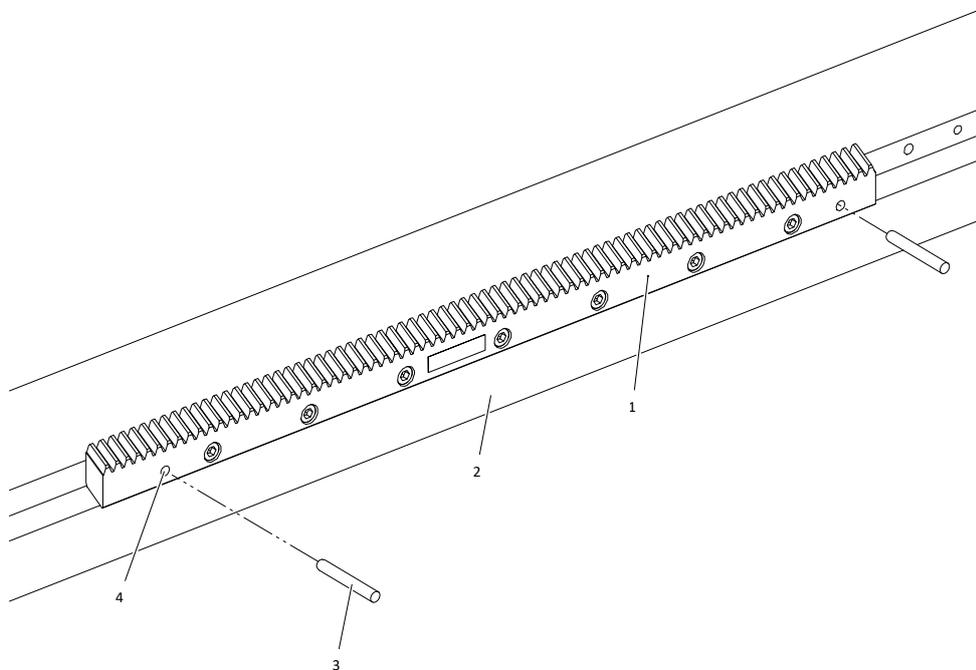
Zahnstange mit Stiften fixieren (Beispiel)
